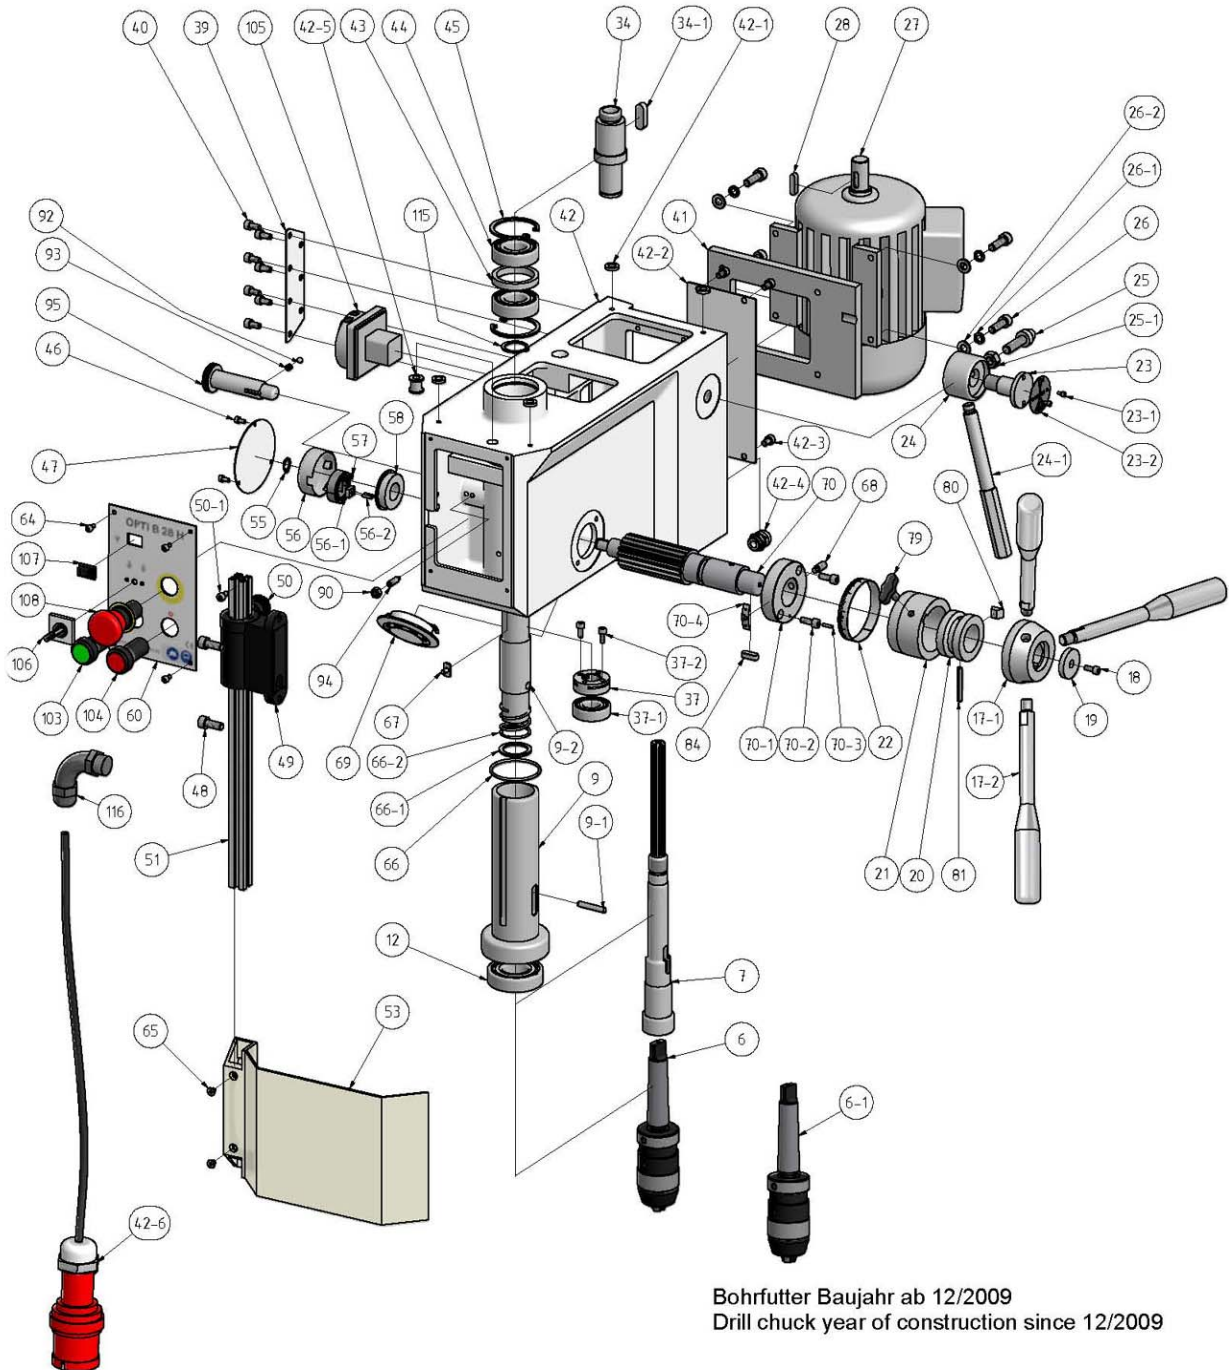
Bohrkopf B28H - Drilling head B28H
